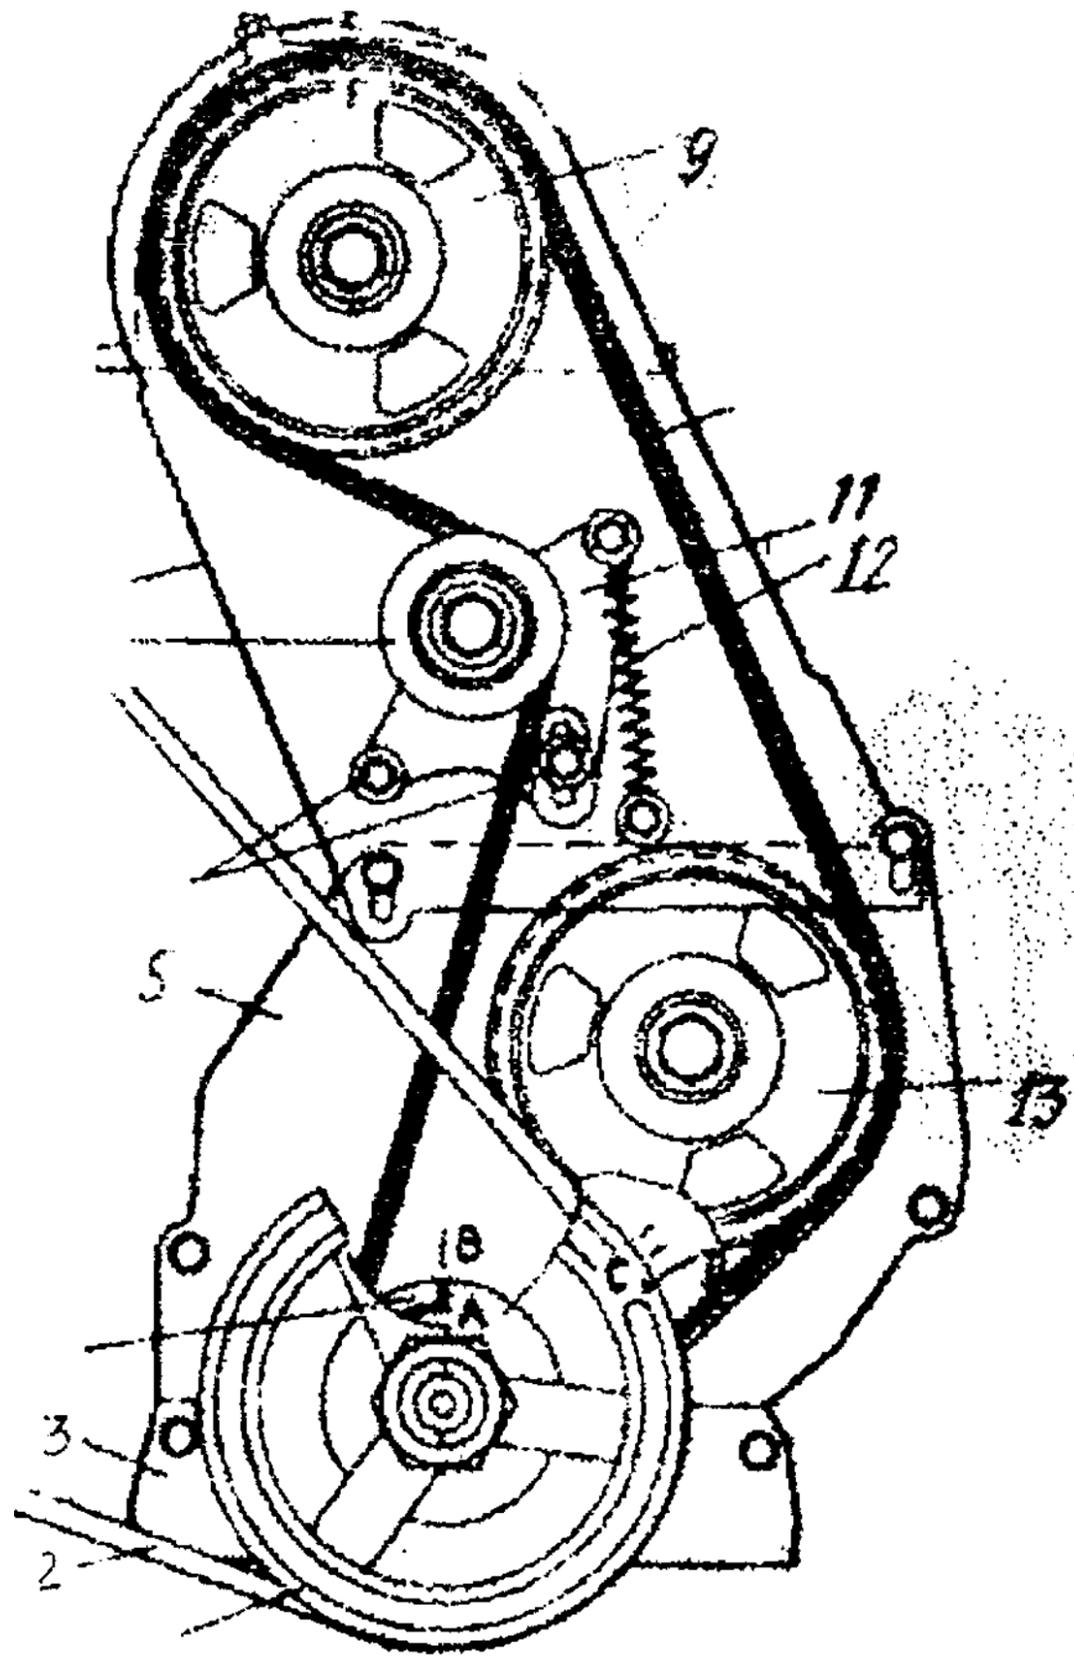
Схема привода механизма газораспределения зубчатым ремнем (ВАЗ-2105): I-
